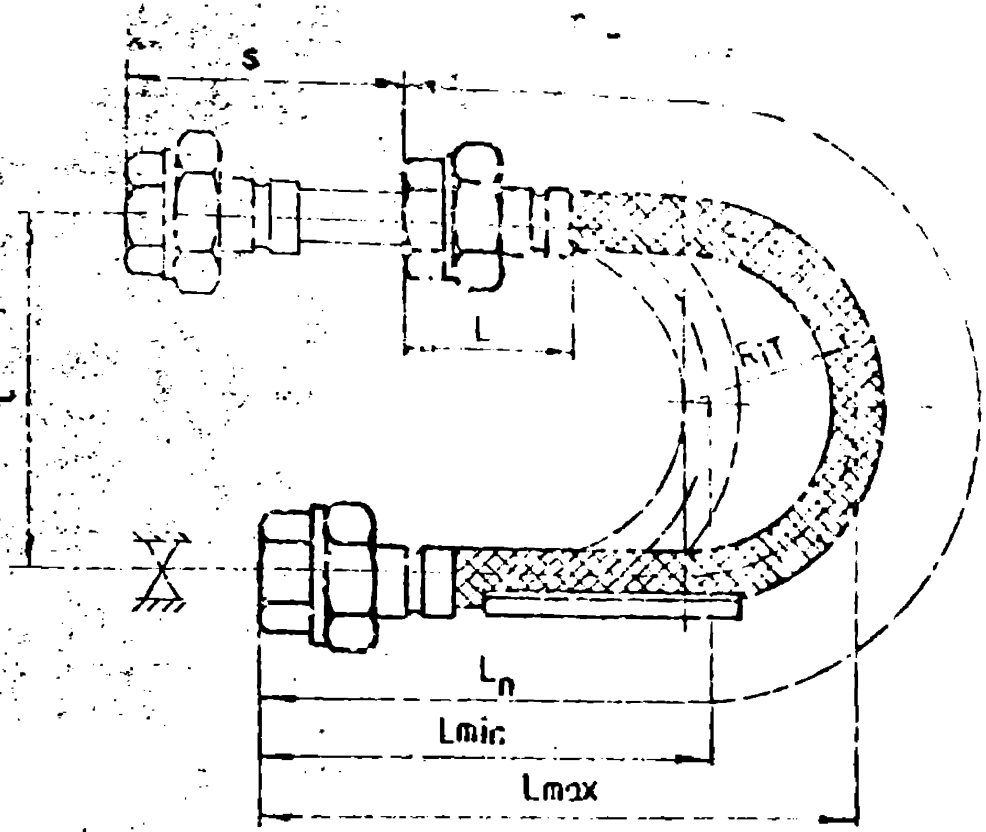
Montaj în arc de 120° orizontal cu un singur capăt mobil.
